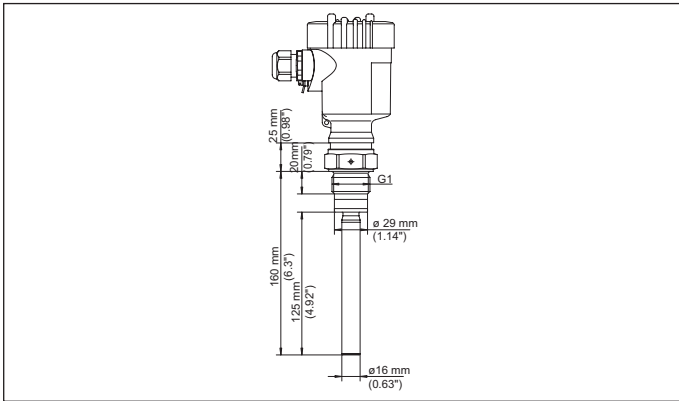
VEGAVIB 61 - Gewindeausführung G1
